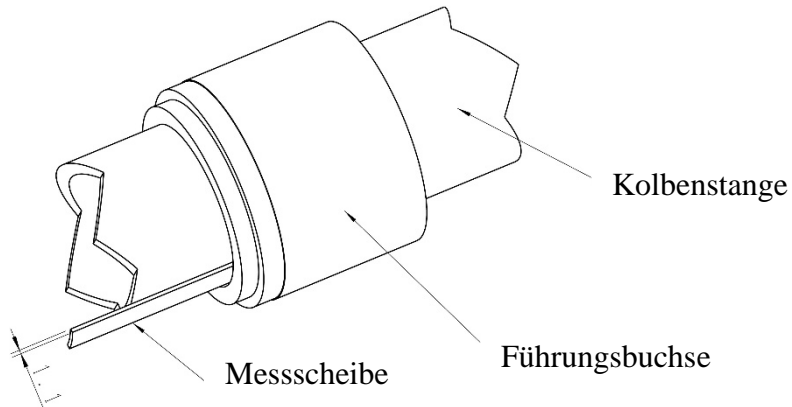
b: Zulässiger Verschleiß an Kolbenstange und Führungsbuchse
